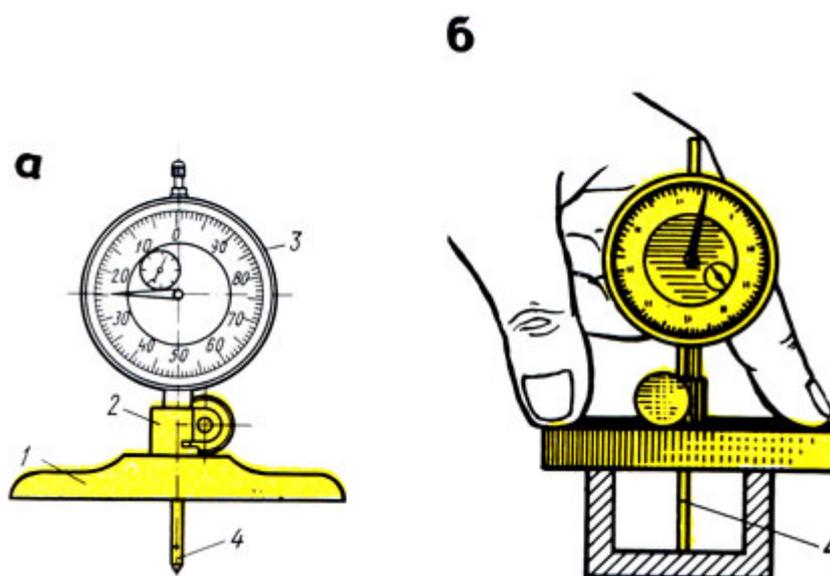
Индикаторный глубиномер: а - устройство, б - прием проверки; 1 - основание, 2 - державка, 3 - индикатор, 4 - измерительный стержень
